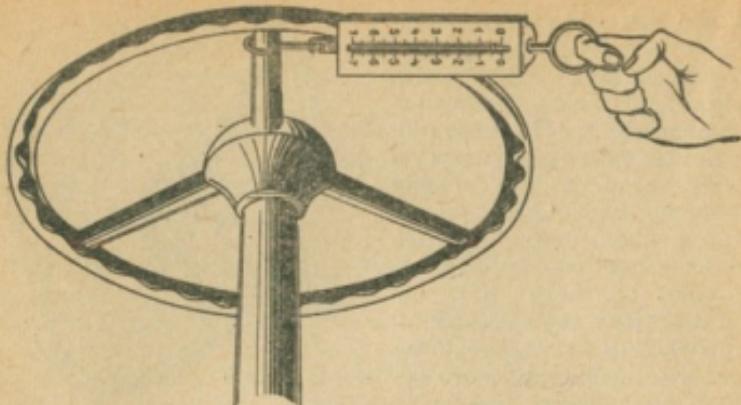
Проверка затяжки подшипников червяка при помощи динамометра
